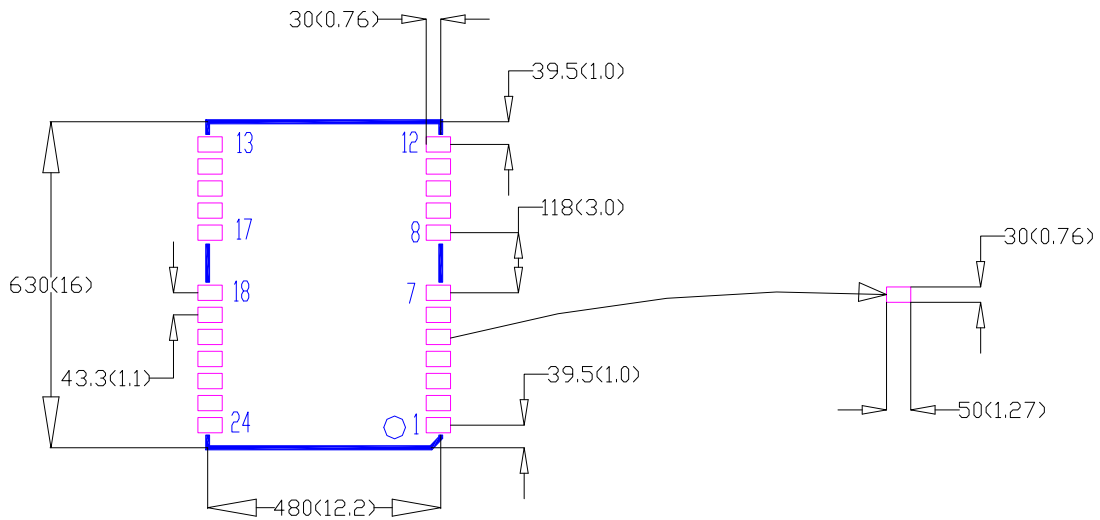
UMD220-IV NV 推荐 PCB 封装设计（尺寸单位：mil，括号内单位：mm）
